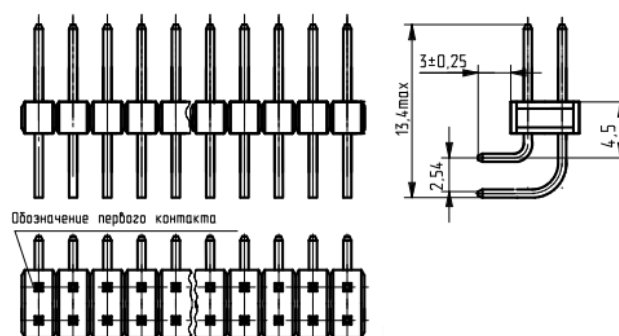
Внешний вид соединителя СНП346-50ВП32
